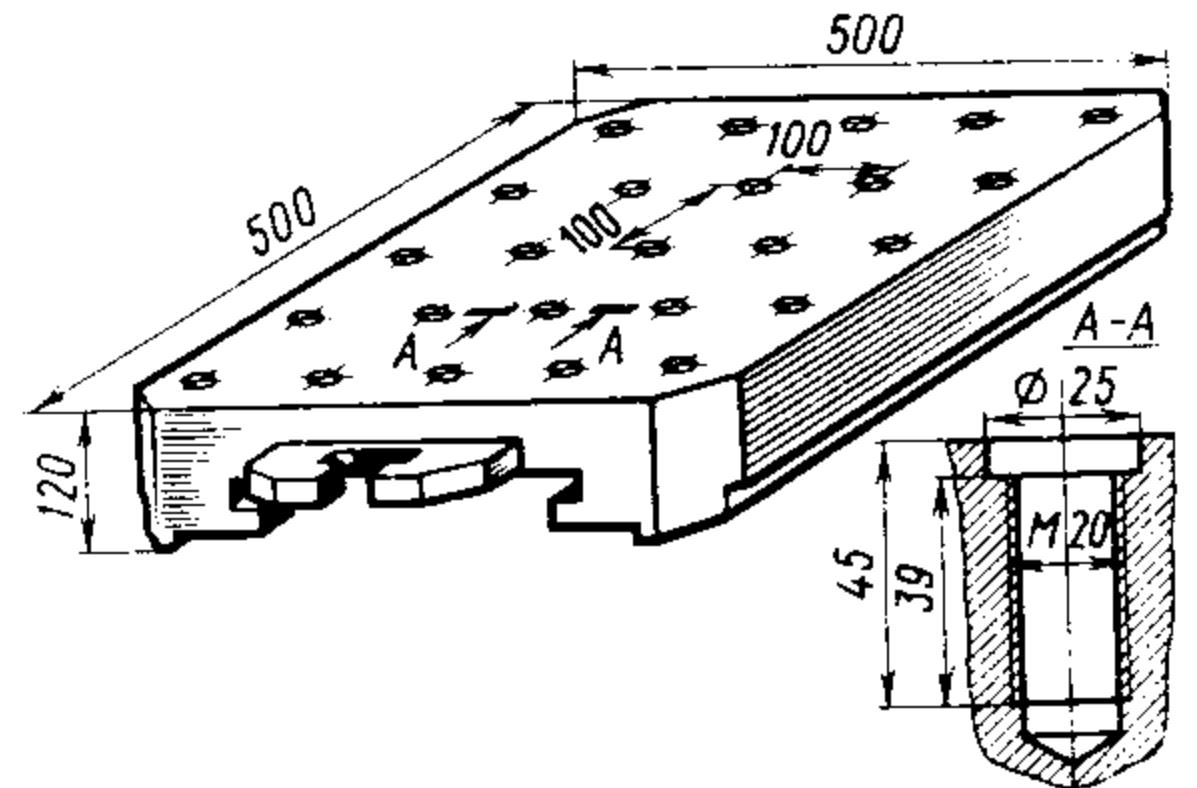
Приспособление-спутник станка ИР-500МФ4
